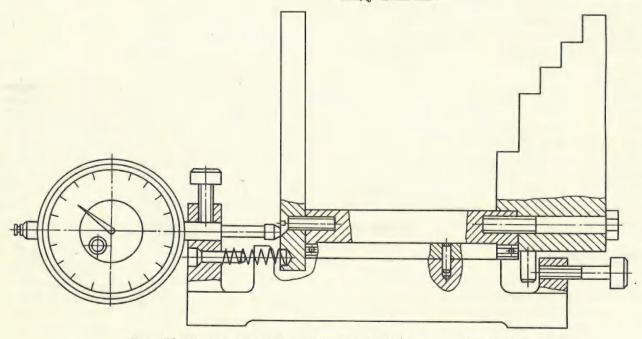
Приспособление для установки резца на шпинделе 🛭 78 мм
